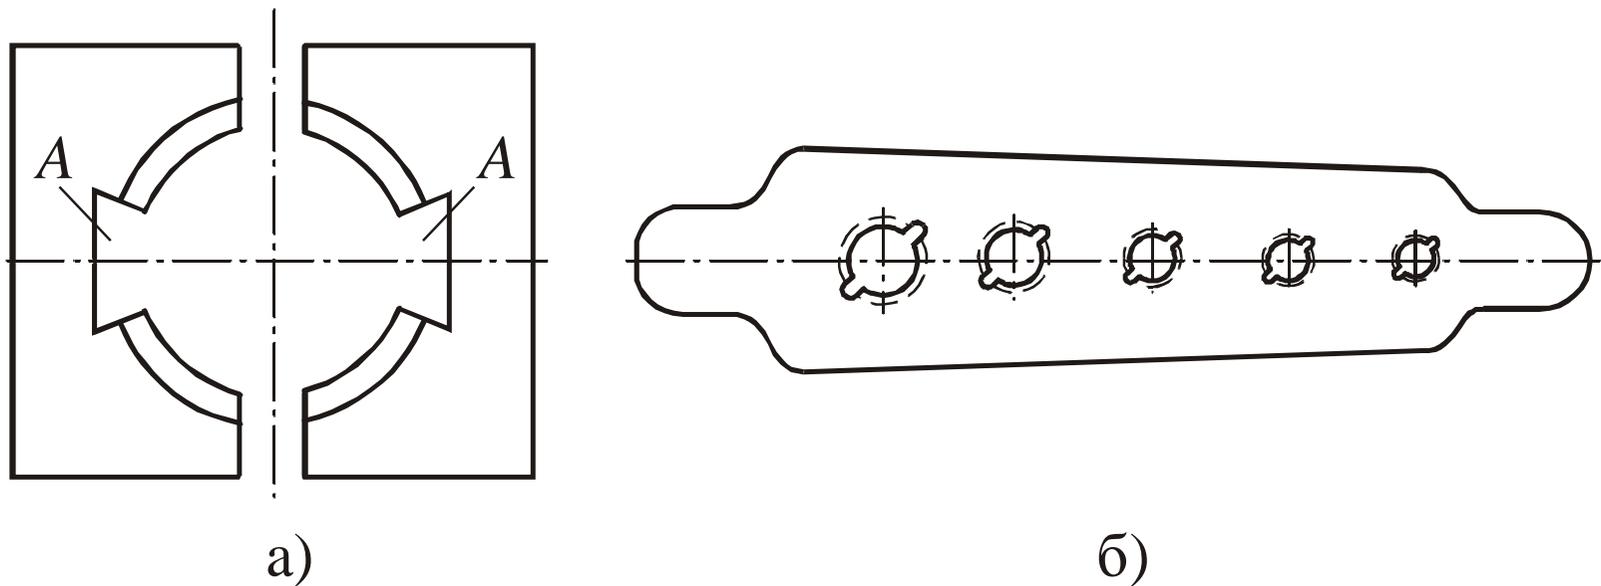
Плашки: *a* – слесарная; *б* – слесарная винторезная дощечка
